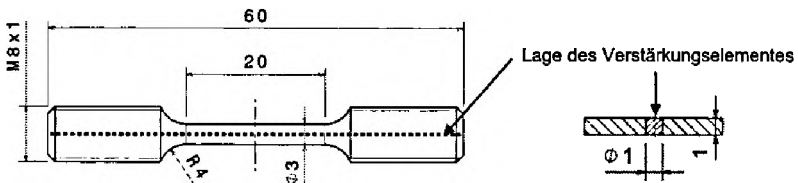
Probengeometrien (Abmessungen in mm), links: Zugversuchsprobe, rechts: Push-Out-Probe
